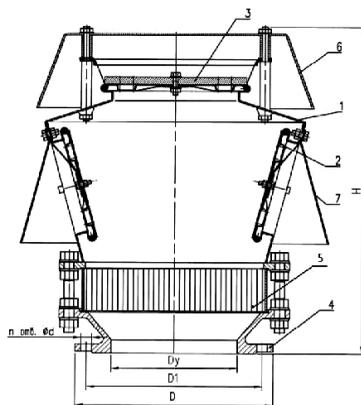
Клапан тип КДМ: 1 – корпус; 2 – тарелка вакуума; 3 – клапан давления; 4 – присоединительный фланец; 5 - огневой предохранитель; 6 – крышка; 7 - козырек
